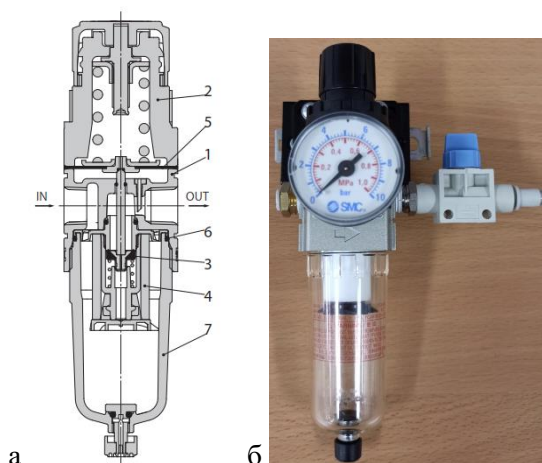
Конструкция (а) и внешний вид (б) блока подготовки воздуха пневматического лабораторного стенда: 1 – корпус; 2 – кожух; 3 – клапан в сборе; 4 – фильтрующий элемент; 5 – мембрана в сборе; 6 – уплотнение; 7 – резервуар
